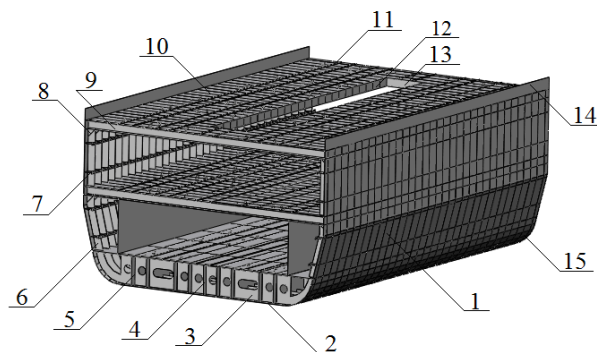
Просторова модель фрагменту ЗП типу “Герои Шипки”: 1 – обшивка борта; 2 – кільовий пояс; 3 – флор; 4 – кіль; 5 – днищовий стрингер; 6 – шпангоут; 7 – бортовий стрингер; 8 – книця; 9 – бімс; 10 – настил палуби; 11 – рейка; 12 – комінгс люка повздовжній; 13 – комінгс люка поперечний; 14 – ширстрек; 15 – лист скулової обшивки
